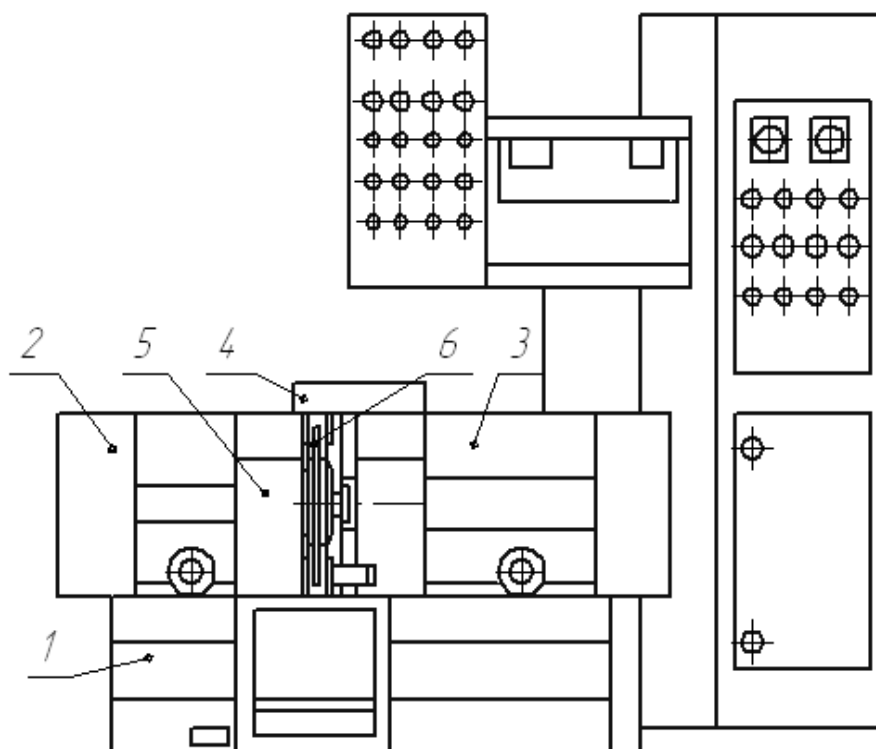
Загальний вид двостороннього торцешліфувального верстату 3342 АДО
